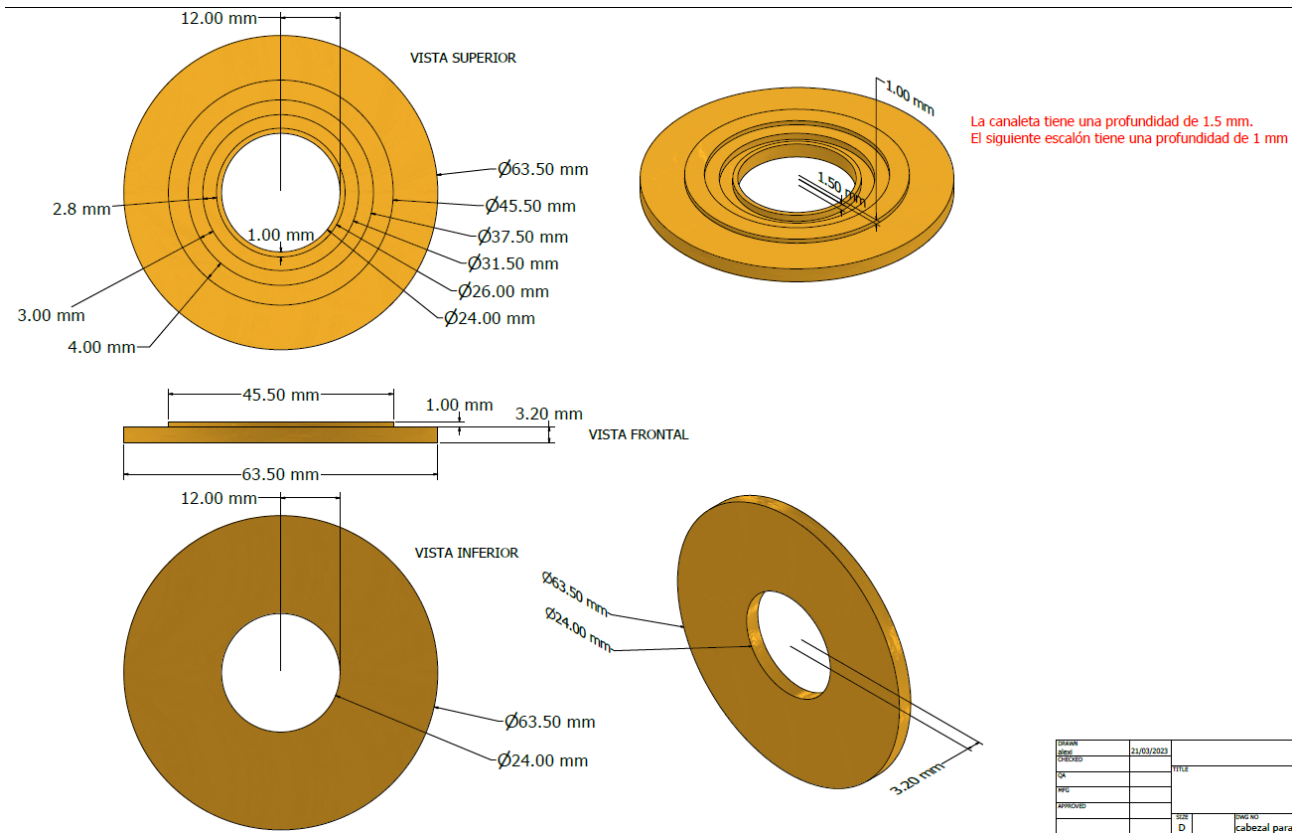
Pieza "C1" de latón que ensambla con tubo de alúmina.
